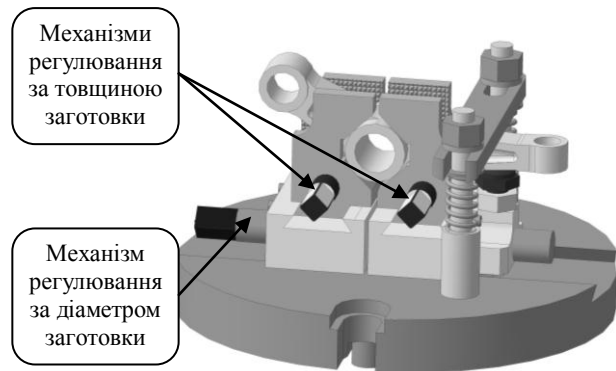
Переналаджуваний установлювально-затискний модуль для обробки деталей типу важелів
